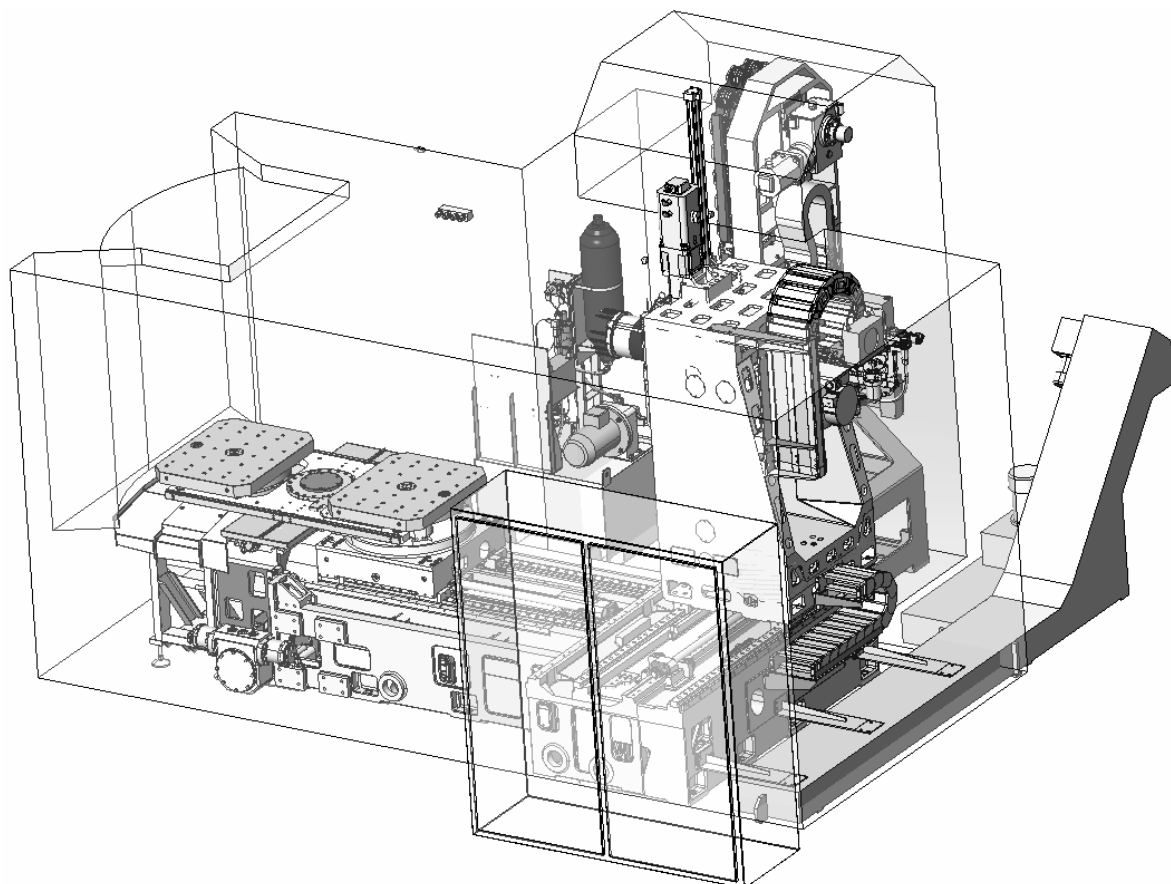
Конструкторская 3D-модель обрабатывающего центра
